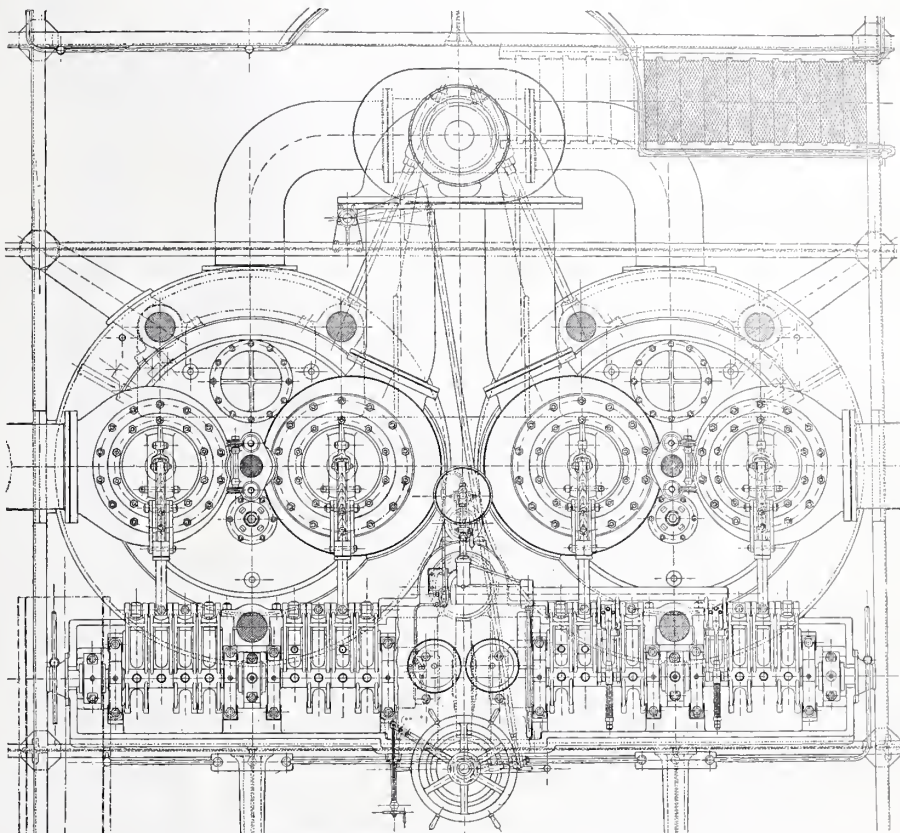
Grundriss (Schnitt zwischen den Cylindern) 1:50.
